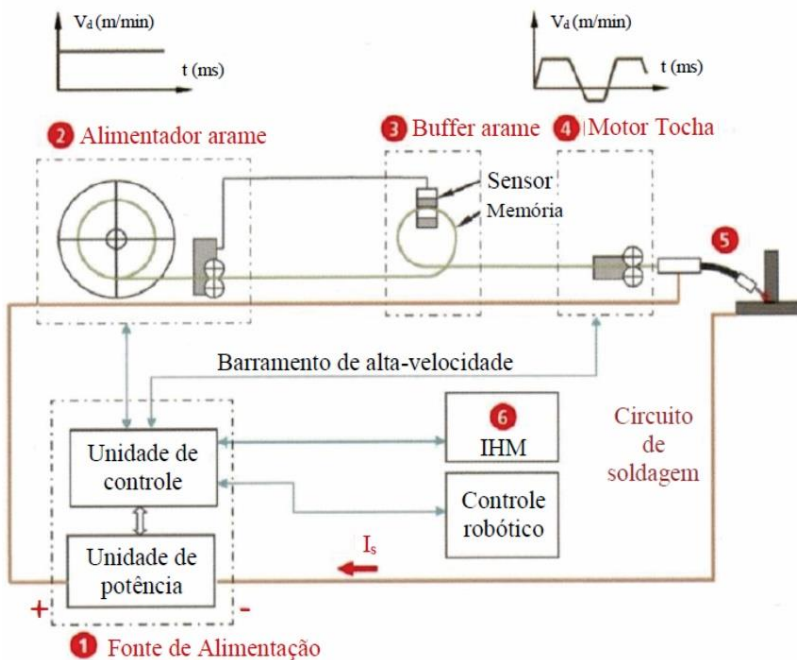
Esquema básico do sistema de soldagem CMT [51]
